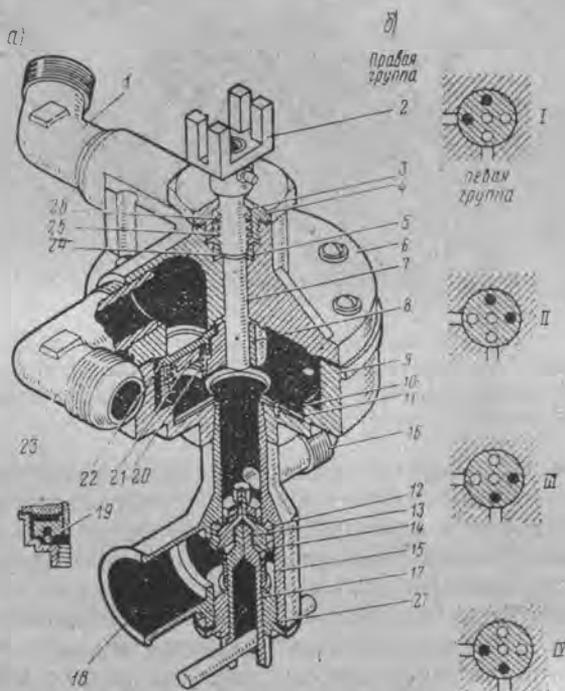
Четырехходовой топливный кран 625000: а — устройство крана: 1 — штуцер (угольник); 2 — наконечник оси кронштейна; 3 — уплотнительное кольцо; 4 — гайка сальника; 5 — шайба; 6 — корпус крана; 7 — ось; 8 — кронштейн; 9 — крышка; 10 — шпилька; 11 — замок; 12 — резиновая шайба; 13 — стопорное кольцо; 14 — клапан; 15 — корпус сливного крана; 16 — штуцер; 17 — шток; 18 — сливной штуцер; 19 — фиксатор крана; 20 — пружина клапана (золотника); 21 — опорный грибок; 22 — клапан (золотник); 23 — штуцер (угольник); 24 — упорное кольцо; 25 — пружина; 26 — шайба сальника; 27 — пробка; б — схема работы: I — левая группа в двигатель; II — левая и правая группы в двигатель; III — правая группа в двигатель; IV — кран закрыт
